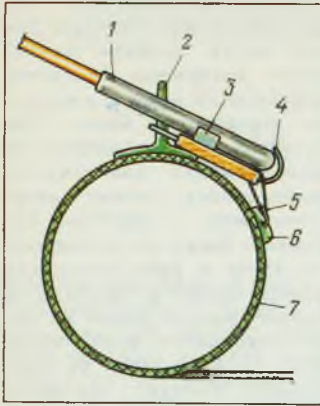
Крепление держателя удильца к лодке: 1 — удочка; 2 — уключина; 3 — уголок; 4 — скоба для удильца; 5 — застёжка; 6 — накладка; 7 — борт лодки.
